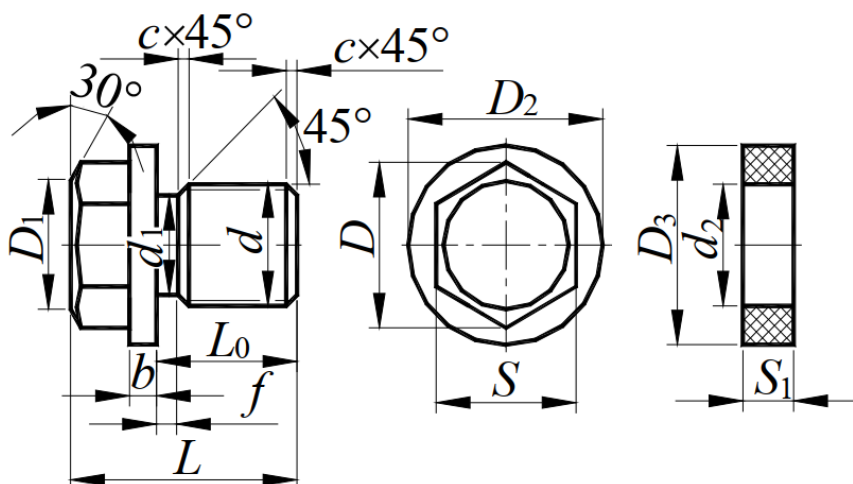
Пробка сливная цилиндрическая с внешним шестигранником
